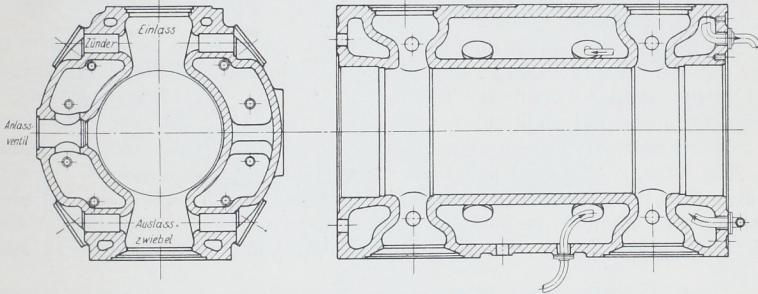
Viertaktgroßmaschinenzylinder, Ausführung der Maschinenfabrik Augsburg-Nürnberg.
